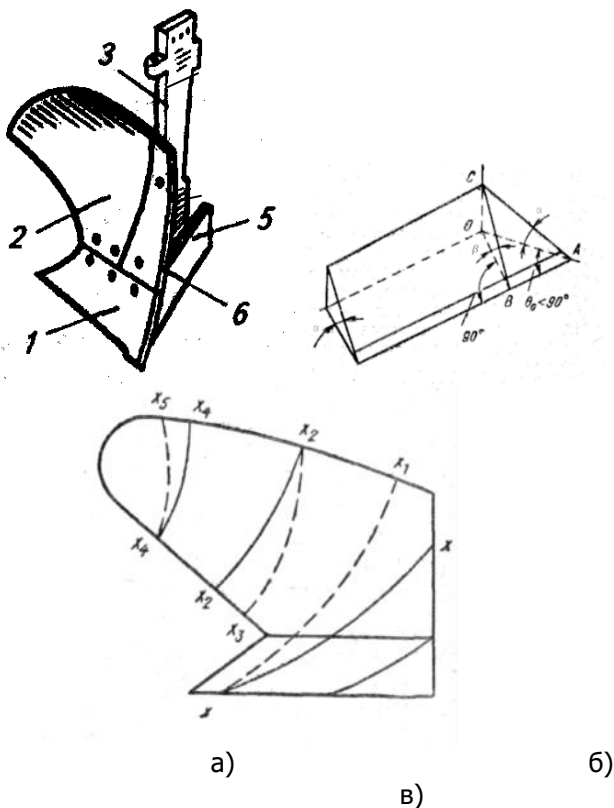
Рабочая поверхность корпуса плуга: а - кинетические параметры лемеха; б - сечения отвала поперечно-вертикальной плоскостью; 1 - лемех; 2 - отвал
